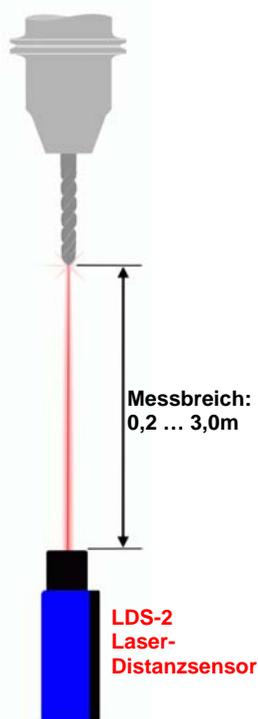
Anordnung des Laserdistanzensors bei der Werkzeuglängenkontrolle in Richtung der Werkzeuglängsachse (z-Richtung)
